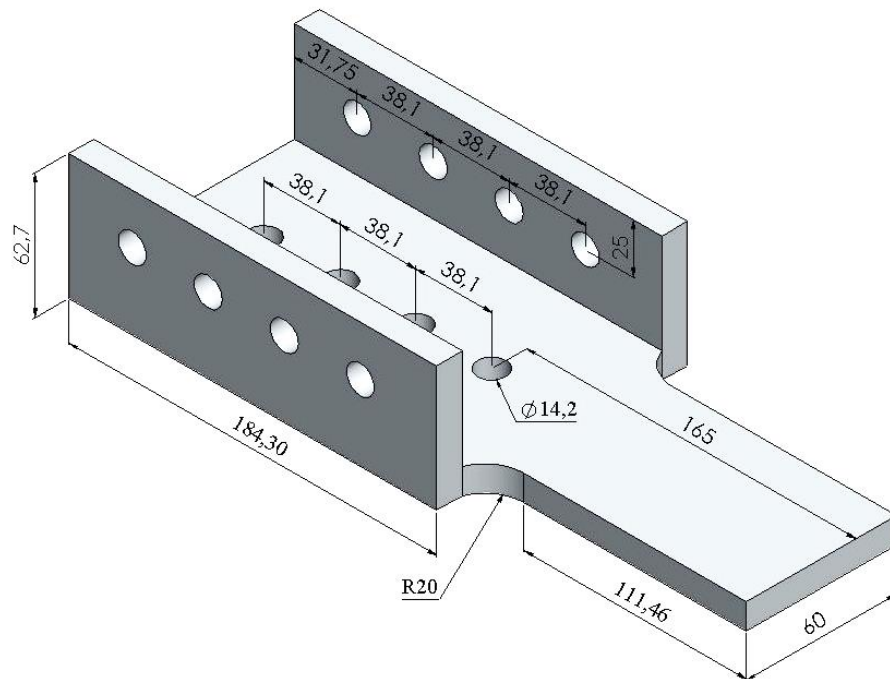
Dispositivo para fixação de perfis U com flanges de 50 mm de altura, dimensões em (mm)
